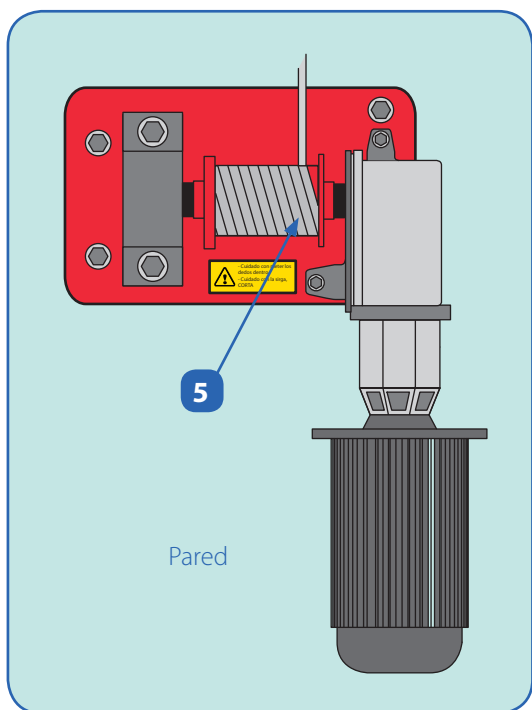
Detalle Torno EXTREMO Automático a pared.
